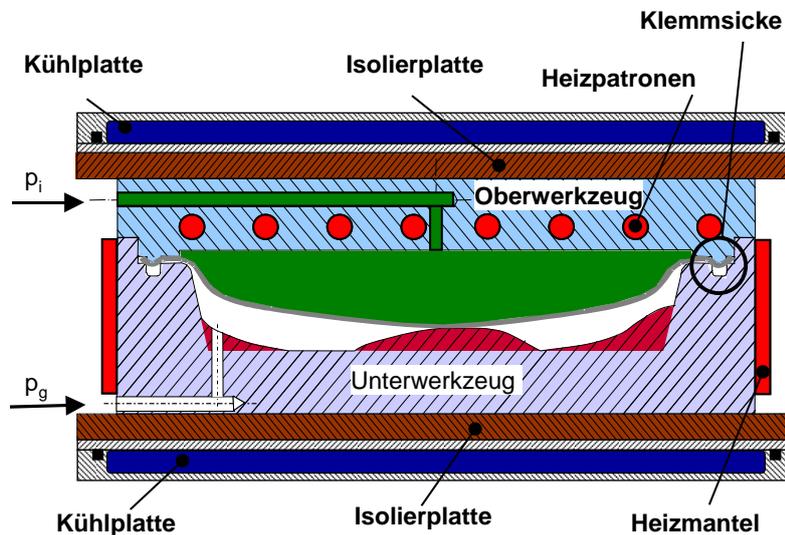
Prinzipieller Aufbau eines Werkzeuges für die Superplastische Blechumformung
